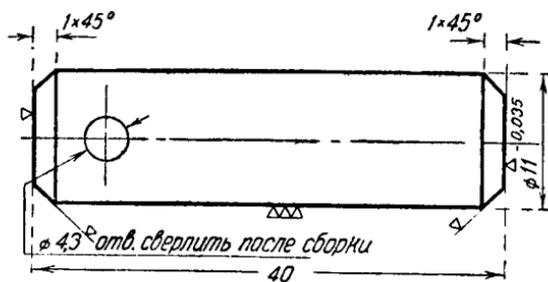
Дет. 18-28. Палец к корпусу подшипника
